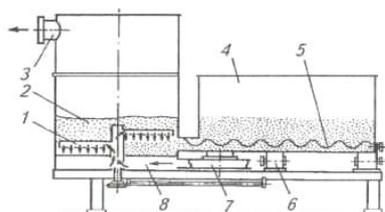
Схема дымогенератора: 1 - ворошитель; 2 - деревянные опилки; 3 - дымовой патрубок; 4 - бункер для древесных опилок; 5 - подающий шнек; 6 - привод; 7 - вентилятор; 8 - воздухораспределитель
